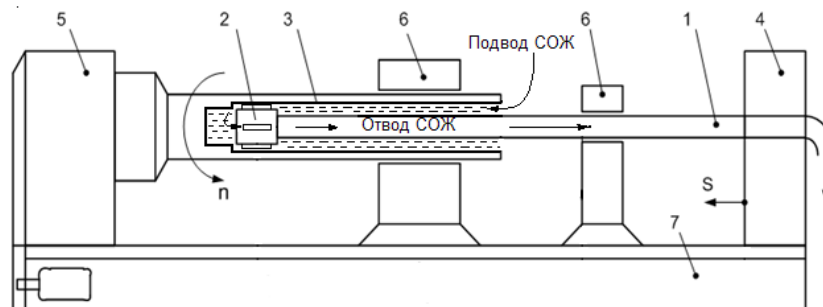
Эквивалентная механическая модель токарного станка. Обозначения: 1 - стембель борштанги, 2 - расточная головка, 3 - обрабатываемая деталь, 4 - суппорт, 5 - шпиндельная бабка, 6 – люнет, 7 – станина
